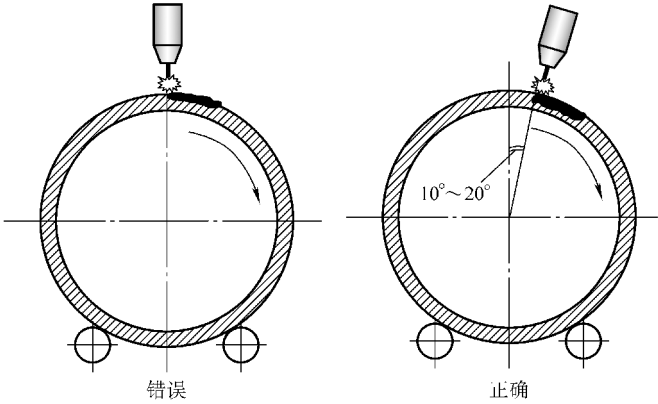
环缝半自动氩弧焊枪的正确位置
